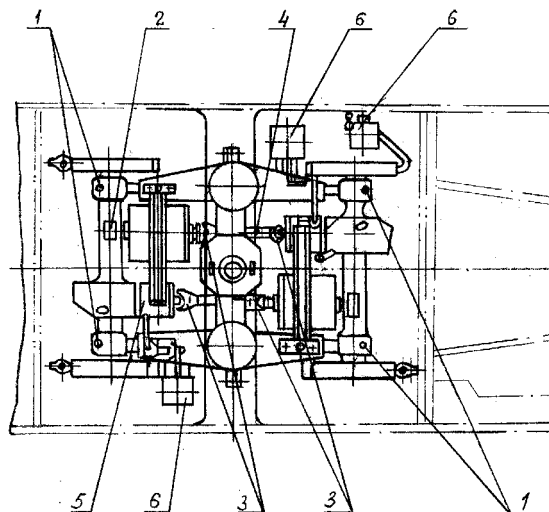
Схема смазки механического оборудования тележки вагона АКСМ-60102: 1 - буксовые роликоподшипники сферические; 2 - подшипники редуктора привода спидометра; 3 - карданный вал: игольчатые подшипники и манжеты; 4 - шлицевое соединение карданного вала; 5 - шарнирные и трущиеся соединения колодочно-барabanного тормоза; 6 - тормозной электромагнит
